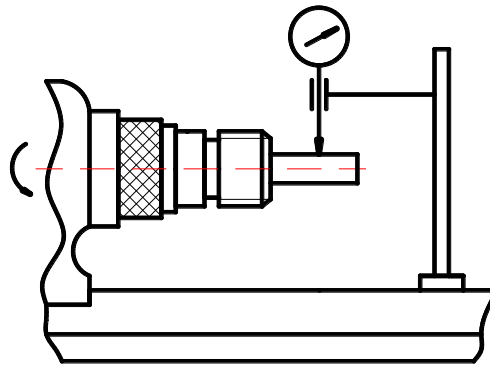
Проверка радиального биения цилиндрической оправки
